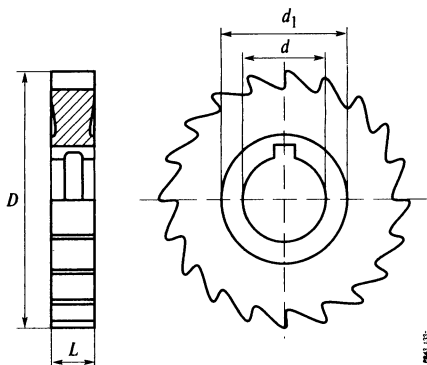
Металлические дисковые фрезы без бокового зазора с крупным зубом
